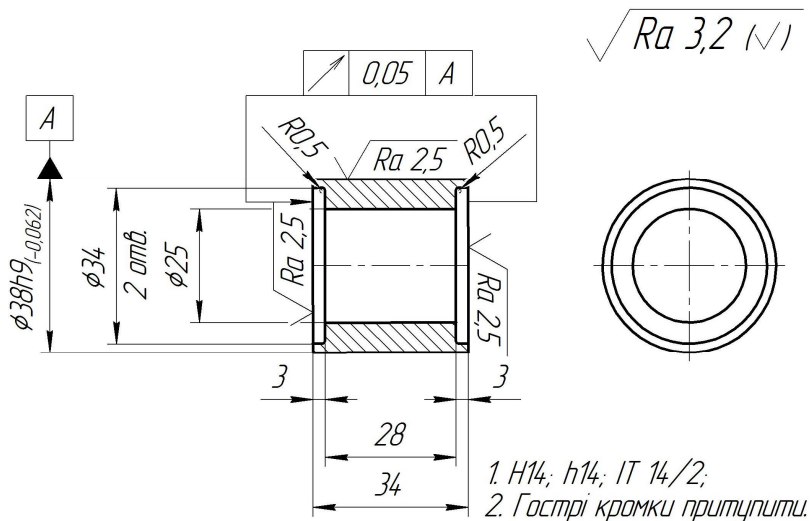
Фрагмент робочого креслення деталі типу «втулка»
